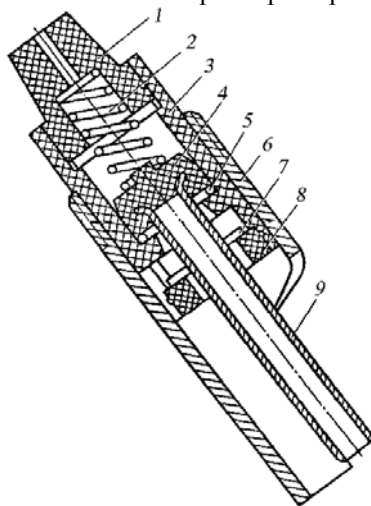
Автонапувалка АС-Ф-25 для свиней:
